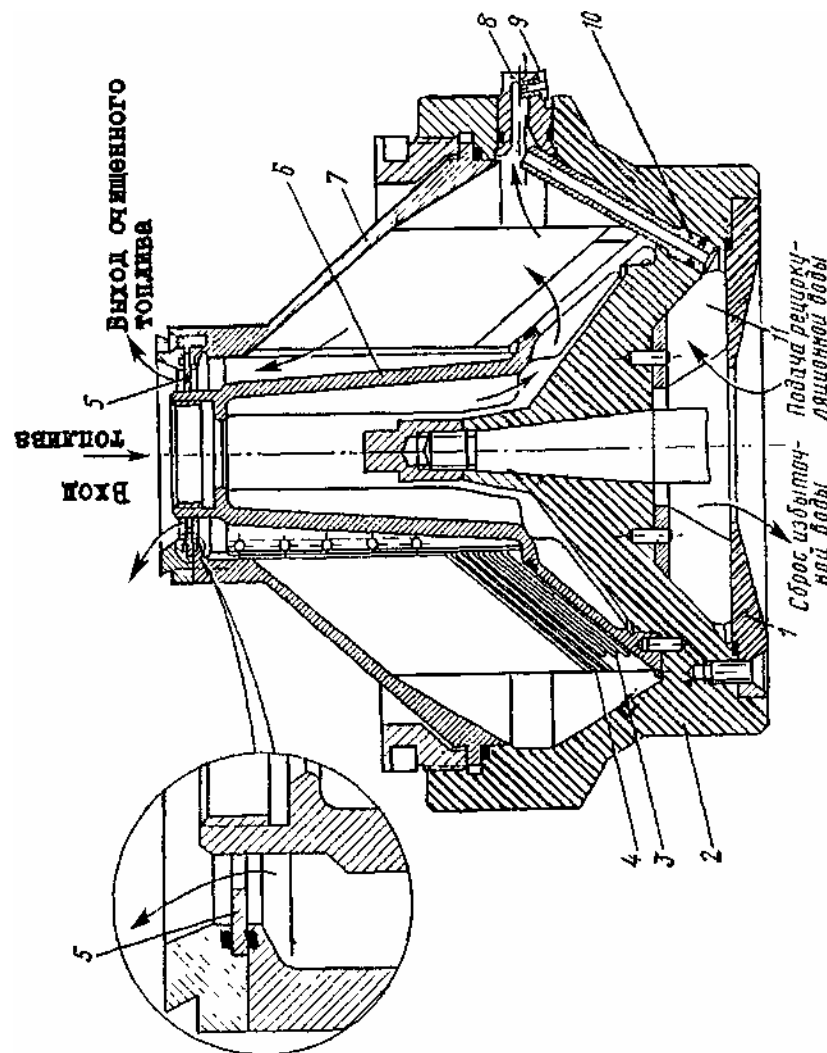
Схема конструкции соплового барабана типа "Гравитроль" 1-нижняя регулировочная шайба; 2-корпус барабана; 3- и 4-малые и большие сепарационные тарелки; 5-верхняя регулировочная шайба; 6-тарелкодержатель; 7-крышка барабана; 8-соплодержатель; 9-сопла (8шт.); 10-рециркуляционные трубки (8 шт.); 11-камера рециркуляционной воды.
